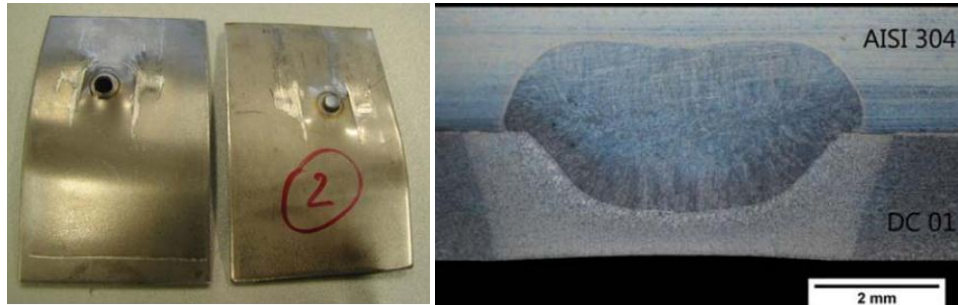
Taille du noyau de soudure (à gauche) et de la macrostructure d'une soudure par points de résistance dissemblable sélectionnée ($I = 7,5 \text{ kA}$) [16].
